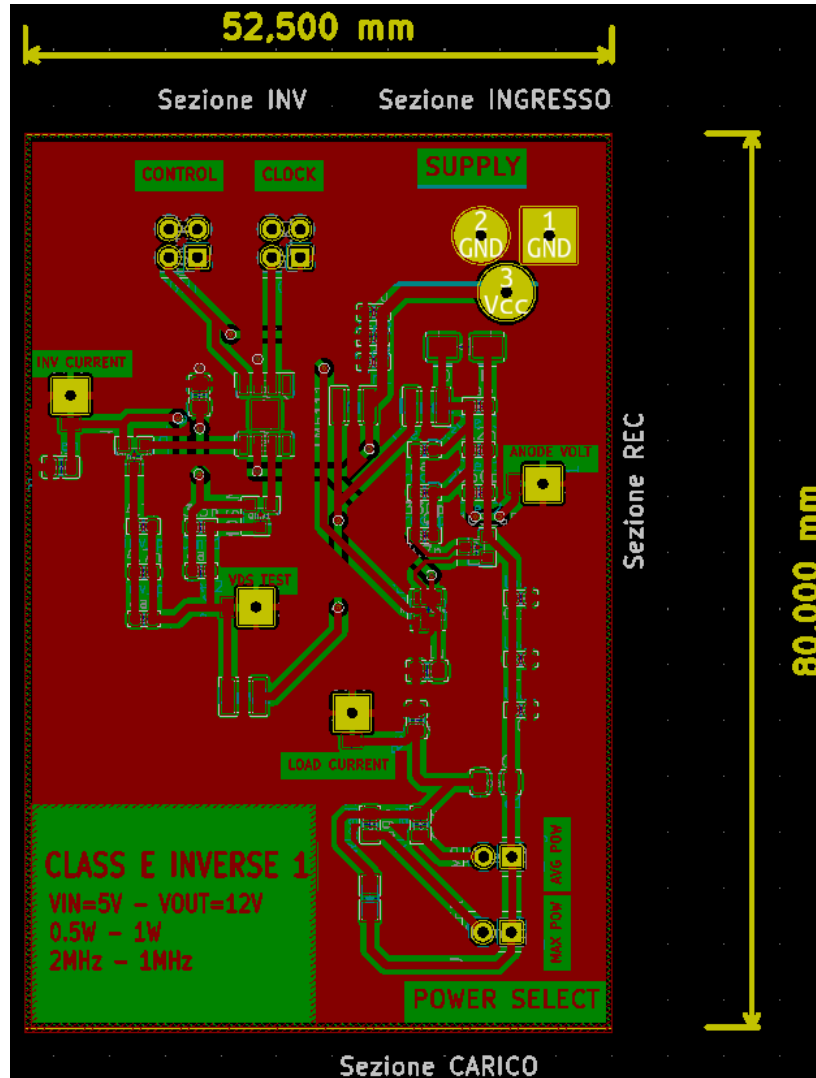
PCB front in KiCad del circuito Inverse1
